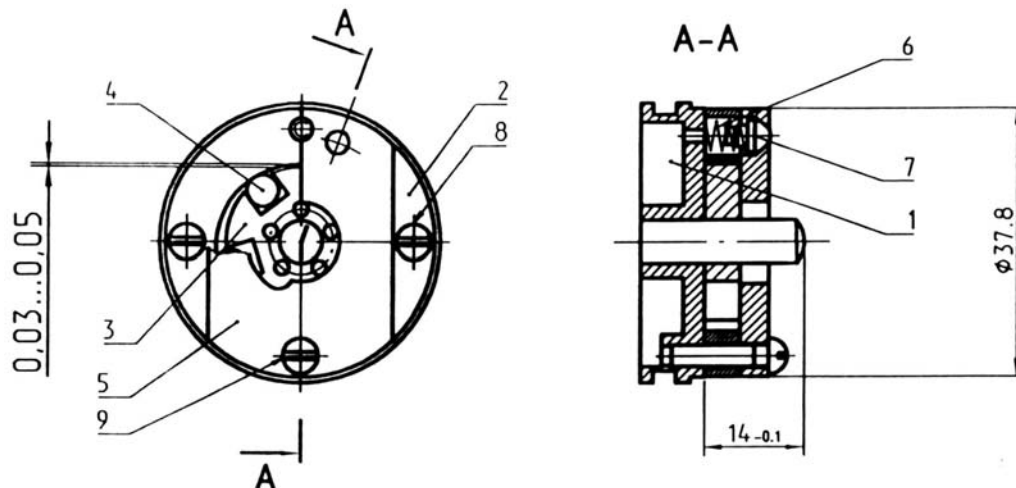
Насос ЭБН: 1 - корпус насоса с осью; 2 - статор; 3 - ротор; 4 - ролик (5 шт.); 5 - крышка насоса, 6 - пружина предохранительного клапана, 7 - предохранительный клапан; 8 - винты крепления статора; 9 - винты крепления крышки насоса
